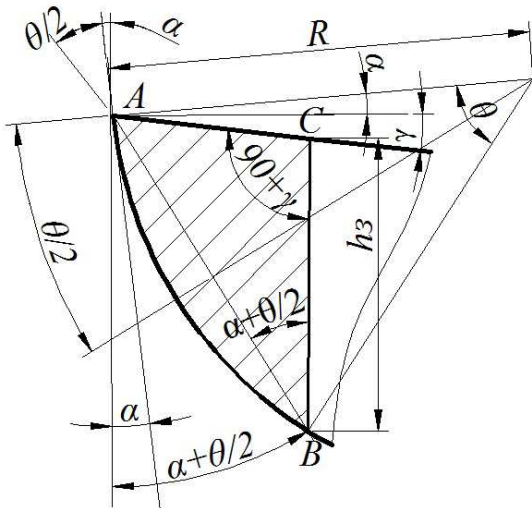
Расчетная схема для объема изношенной части режущей пластины с выпуклой формой задней поверхности
